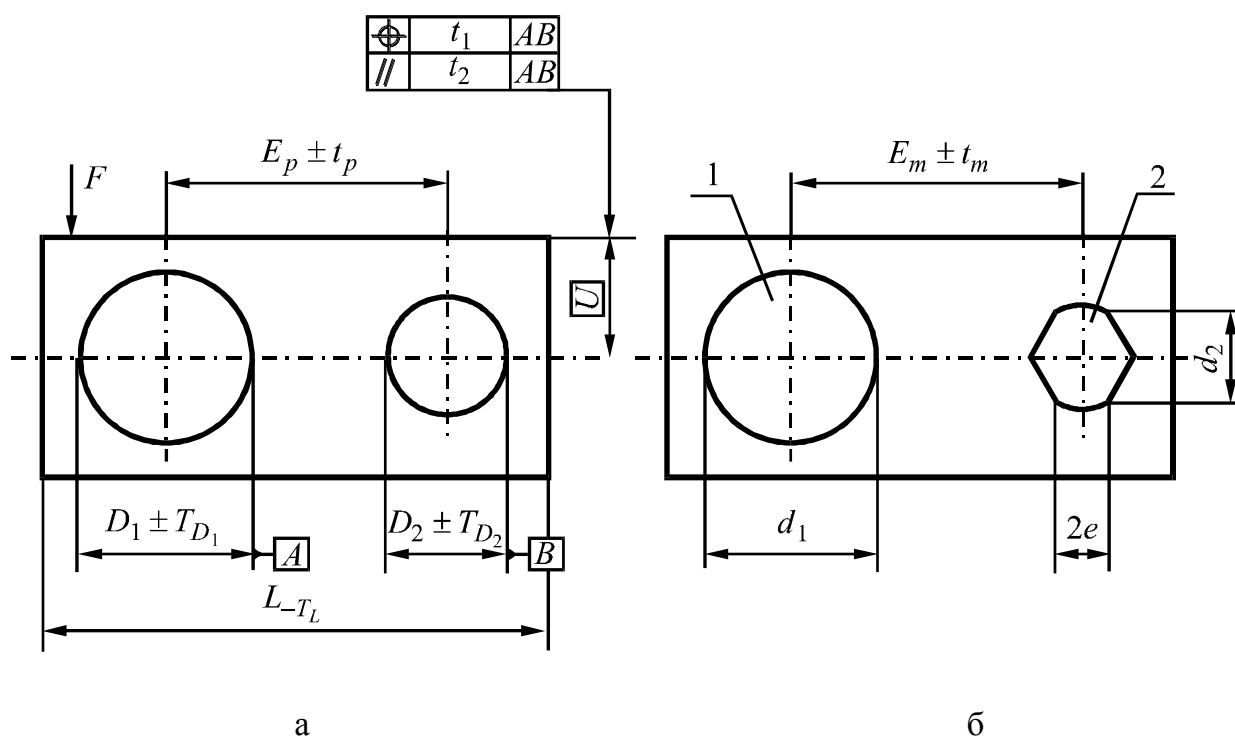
Эскиз детали (а) и приспособлений (б)
